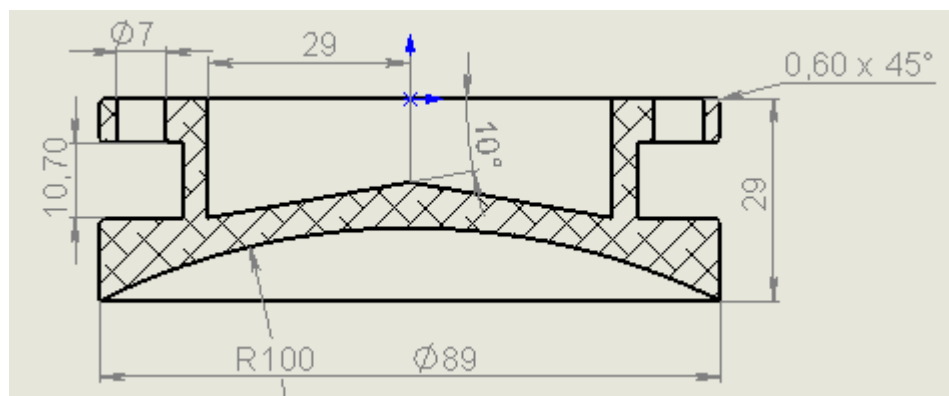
Креслення з габаритними розмірами катоду гармати ВТР-100
